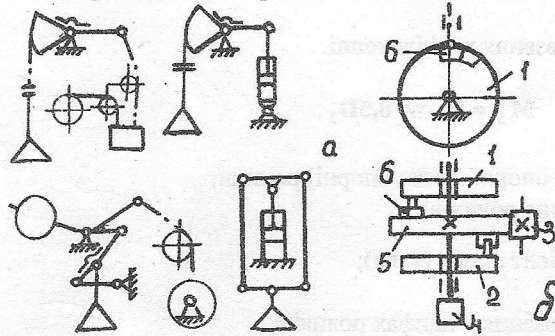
Схеми пристроїв для маневрування конусами (а) і комбінованої лебідки (б): 1, 2-барабан; 3-приводна шестерня; 4-командоапарат; 5-зубчасте колесо; 6-кулачки
